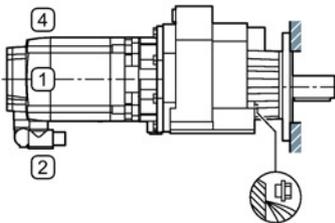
Einbautagen für Stirnradgetriebe ZB und DB, Fuß- Flanschausführung, Baugrößen 39 - 89, 2-stufig und 3-stufig
